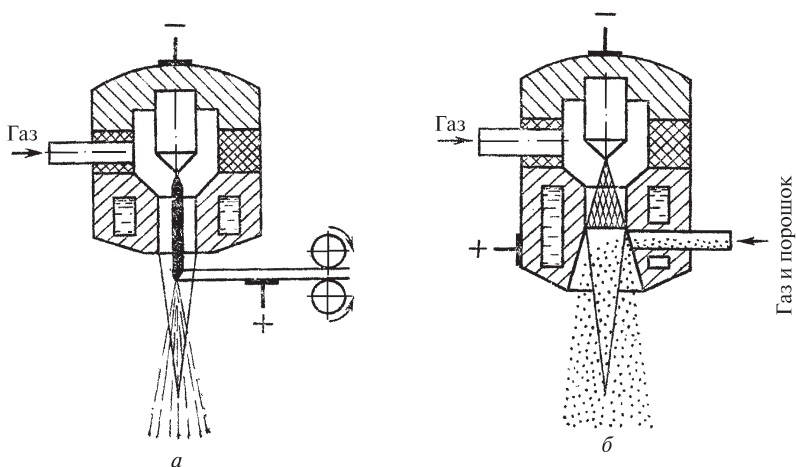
Схема распыления дуговой плазмой токоведущей проволоки (а) и напыляемого порошка (б)
